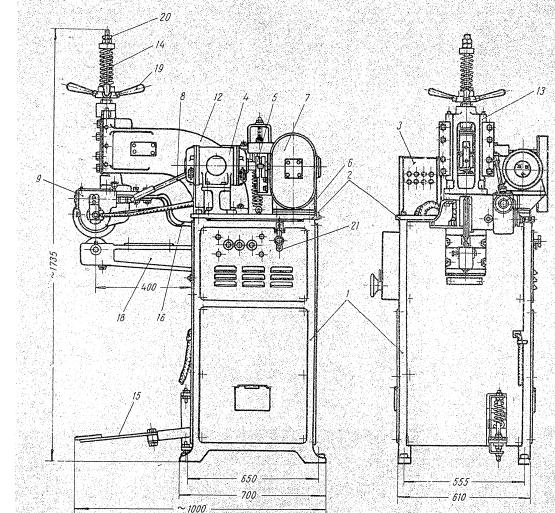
Устройство машины МШМ-50 для продольной сварки.
